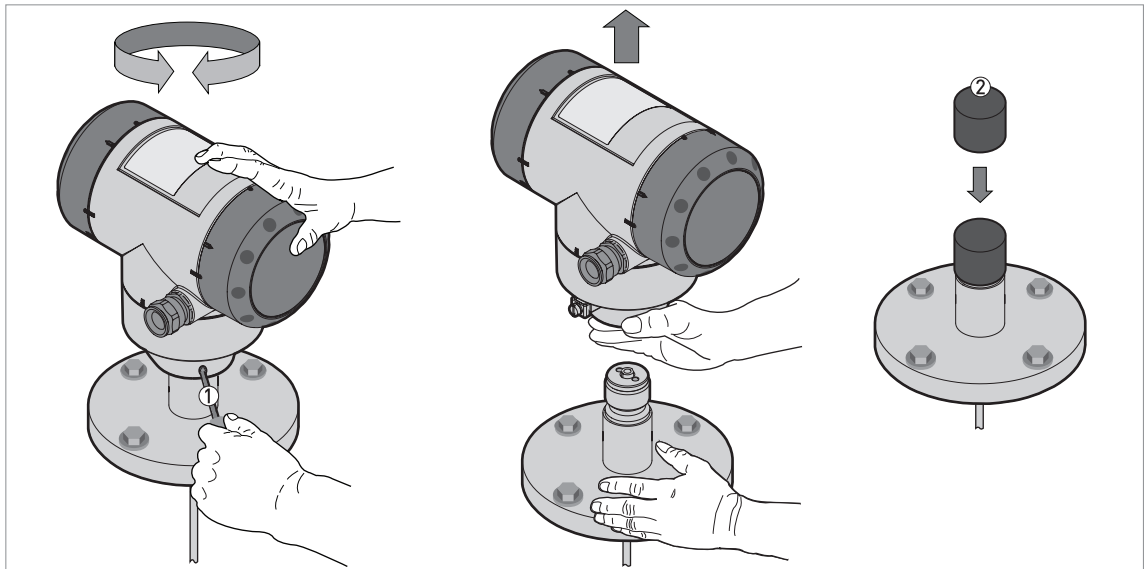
Drehen bzw. Entfernen des Messumformers
